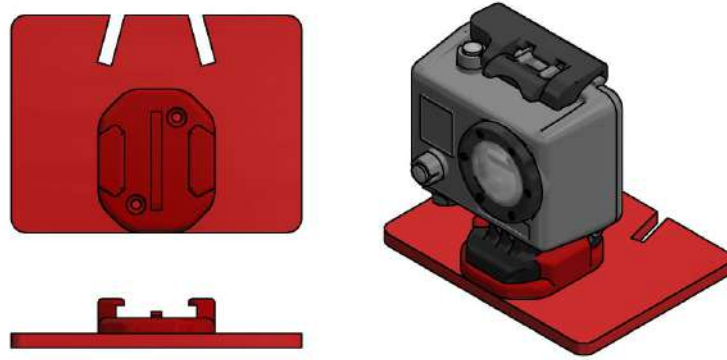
Detalle del ensamble entre la placa inferior y la cámara. Fuente: Elaboración propia.
